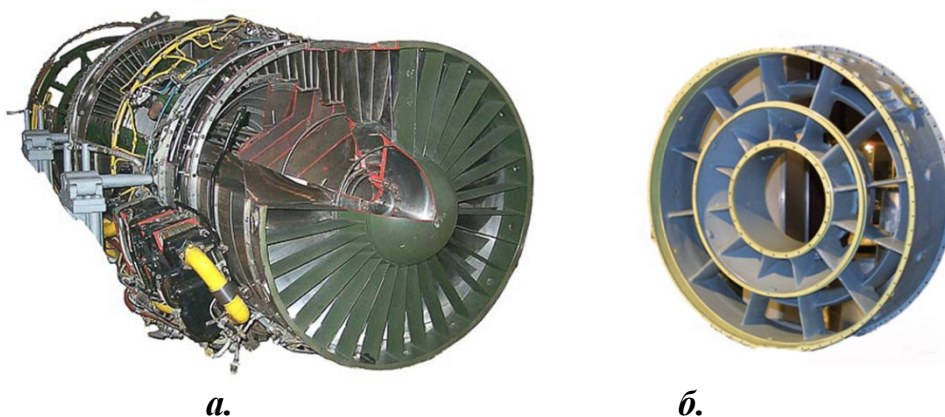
Корпус передньої опори авіаційного двигуна НК-32 (сплав МЛ19) (а), розподільчий корпус (сплав МЛ10) (б).
